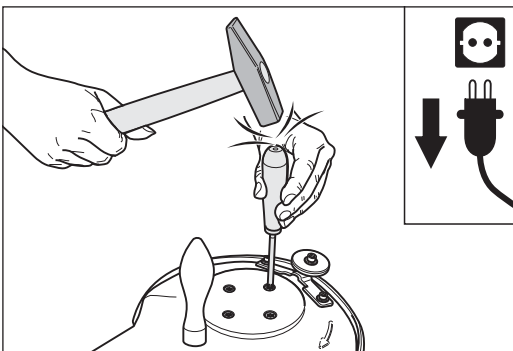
Mit einem geeigneten Schraubendreher mit durchgängiger Klinge und leichten Hammerschlägen die Schrauben der Schleiftellerlagerung lösen.
